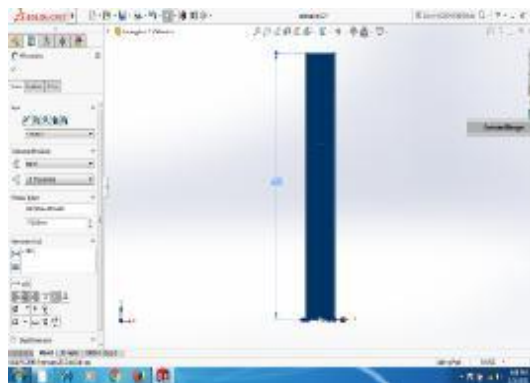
Desain Baja UNP Sebagai Konstruksi Rangka
